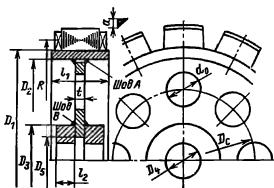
К расчету ротора в виде сварного магнитного колеса.
